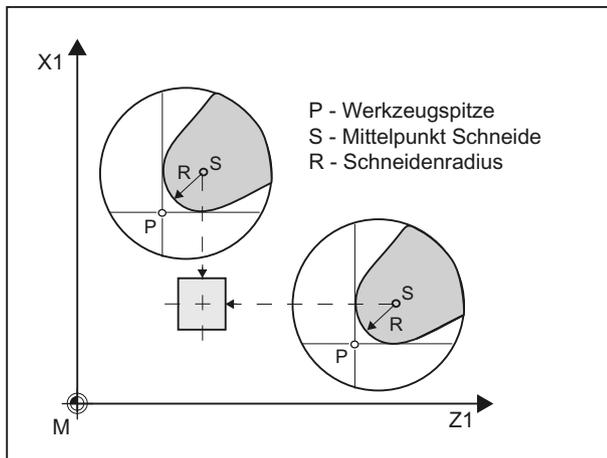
Drehwerkzeug Länge messen: Versatz um Schneidenradius, Beispiel SL=3
